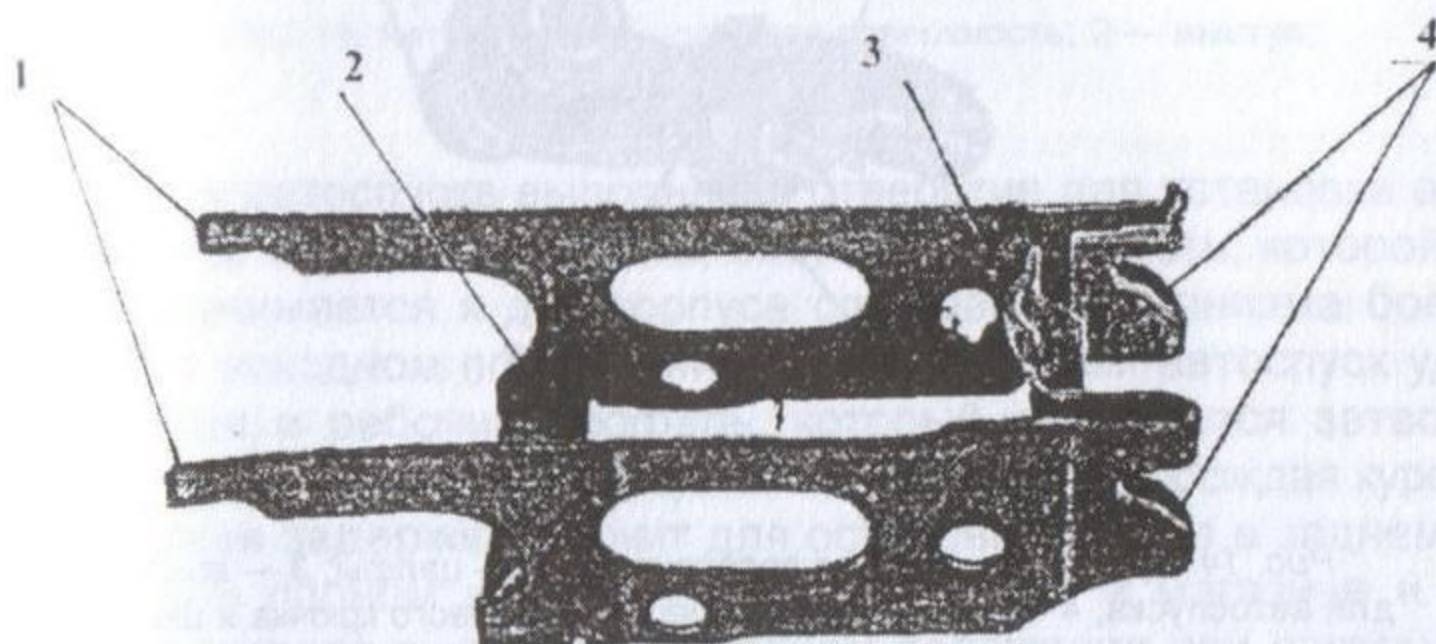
Корпус спускового механизма: 1 — перья; 2 — профиль; 3 — выдавка; 4 — паз
